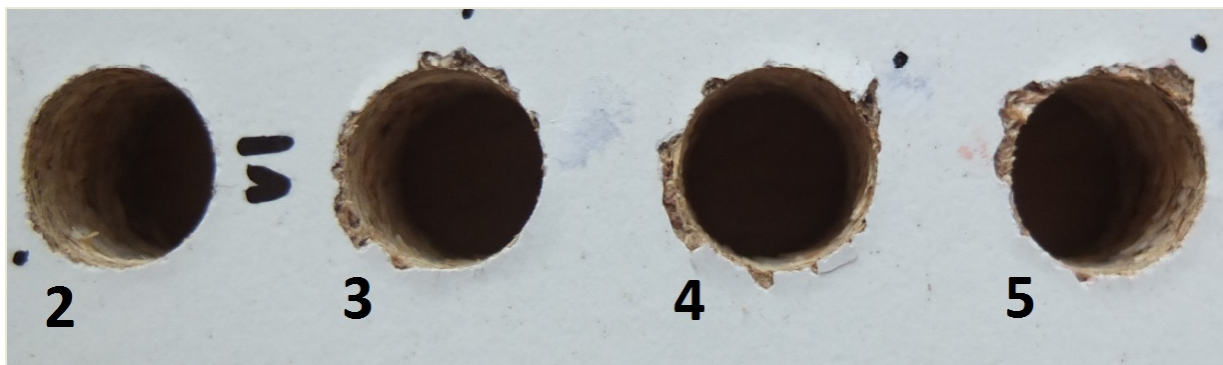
Внешний вид отверстий выполненных сверлом после 2, 3, 4 и 5 циклов затупления (вид со стороны входа инструмента)
